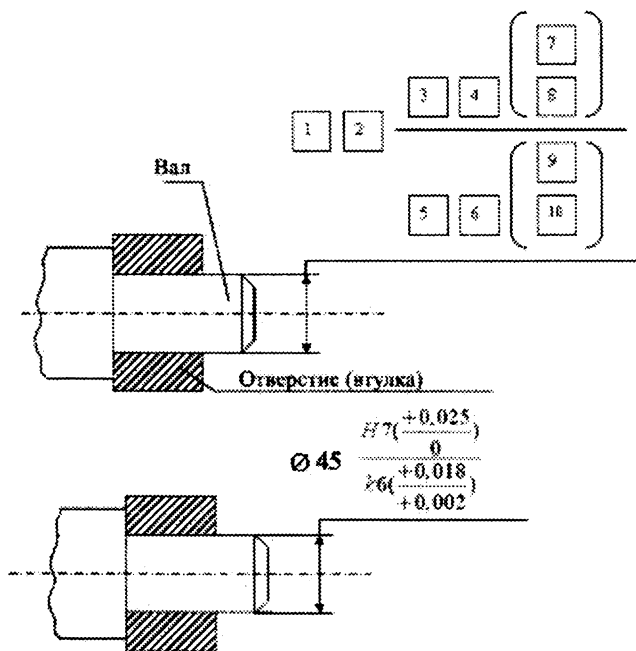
Обозначение посадок на сборочном чертеже:
